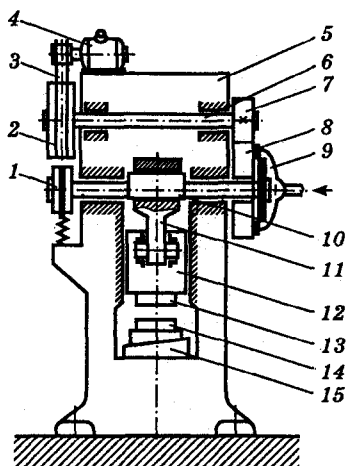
Кинематическая схема кривошипного горячештамповочного пресса
